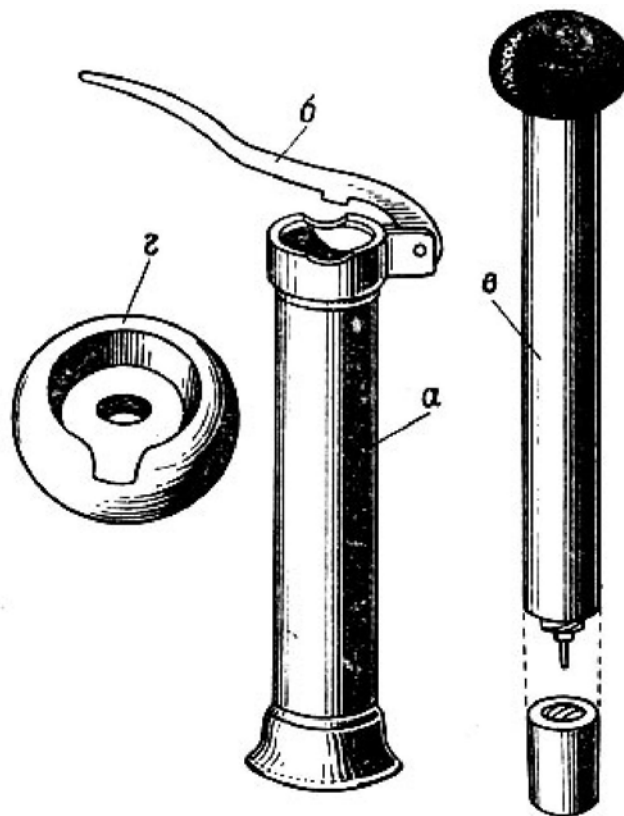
Прибор «Барклай»: а - цилиндр; б - рычаг; в - навойник; з - подставка
